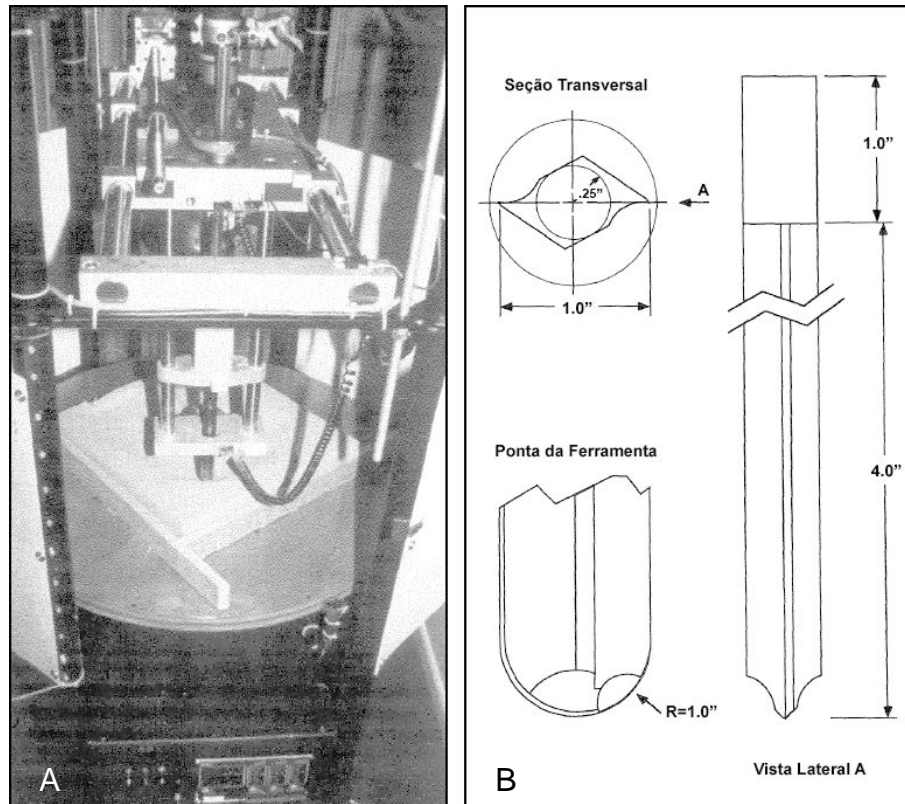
Equipamento (A) e Ferramenta (B) especializados para usinagem de PU flexível.
